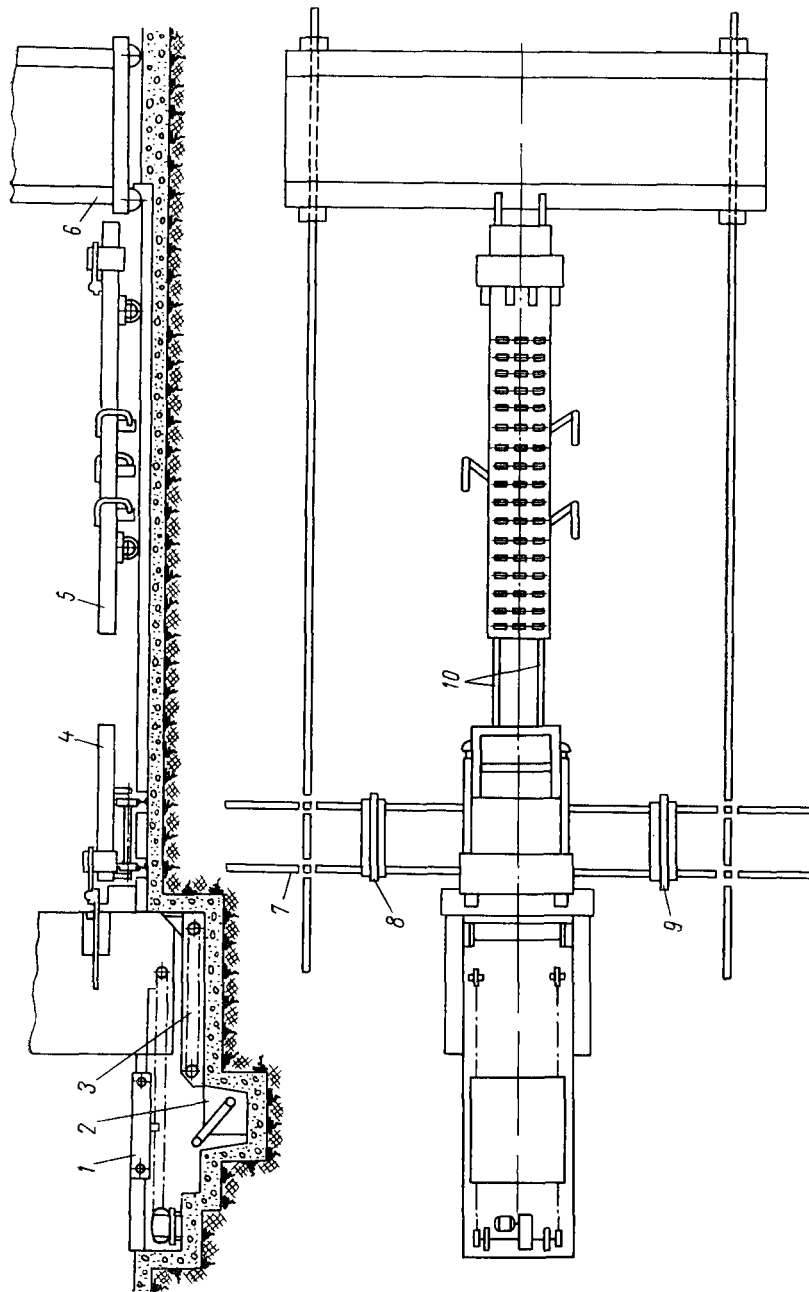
Общий вид комплекса механизмов для резки металла на гильотинных погонцах
